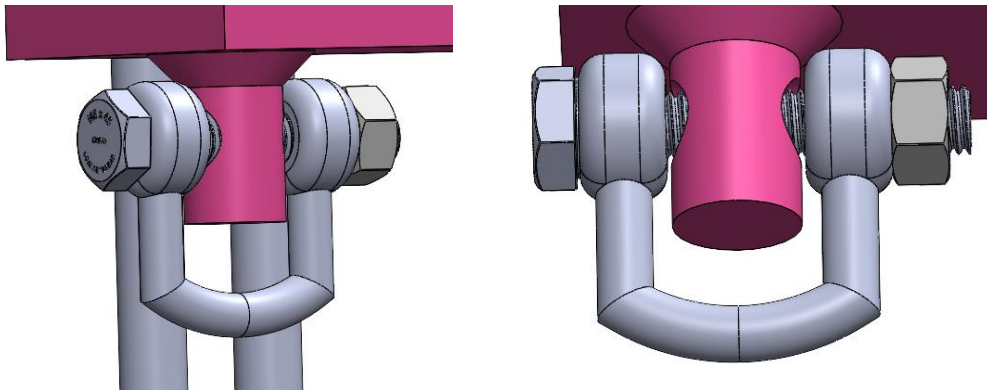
Vistas detalle del enganche tipo mosquetón (Fuente 38)
